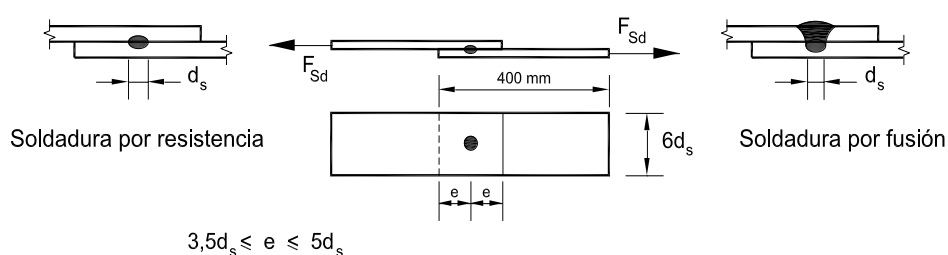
Probeta para ensayo de soldadura por puntos
